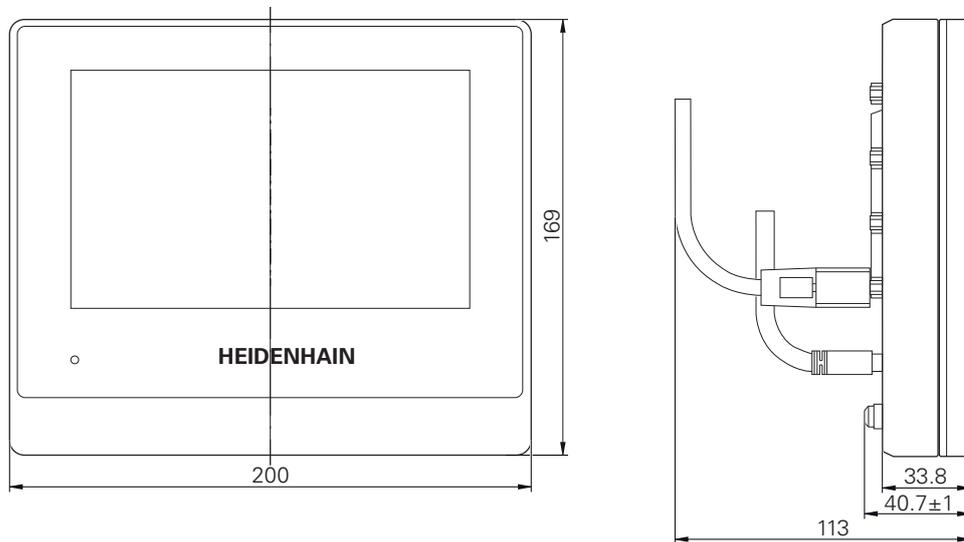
Bemaßungen des Gehäuses der Geräte
